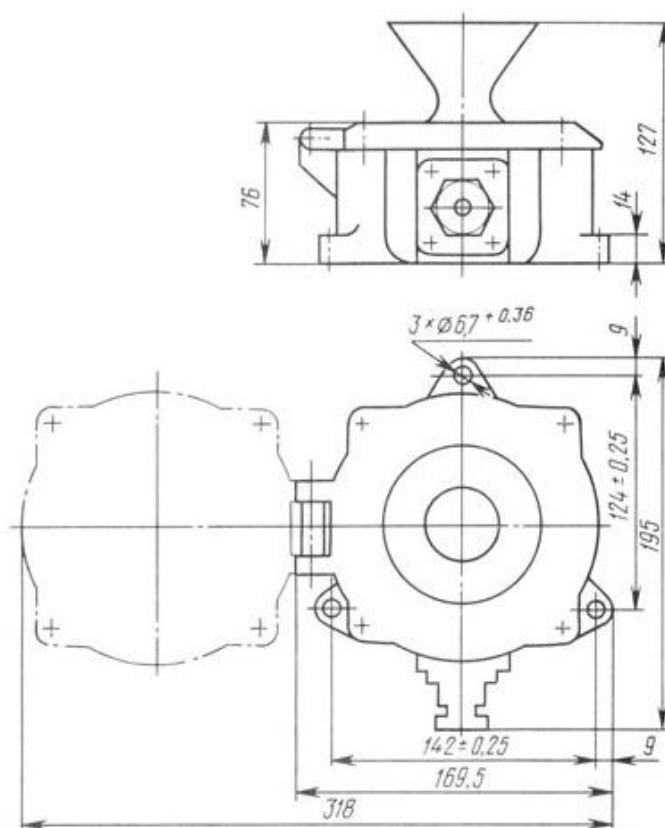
Габаритные и установочные размеры ревуна РВП-220V
